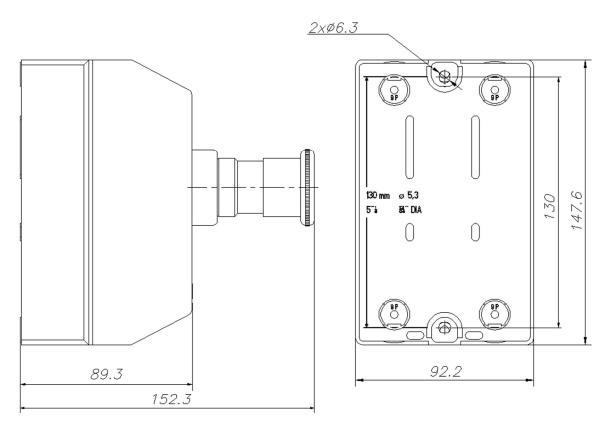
Габаритные и присоединительные размеры NS2-MC01
